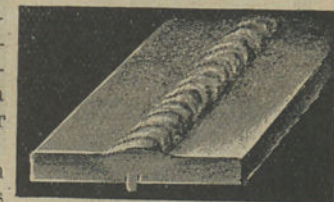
Colagem na base da soldadura, revelada pelo ensaio de corrosão.
